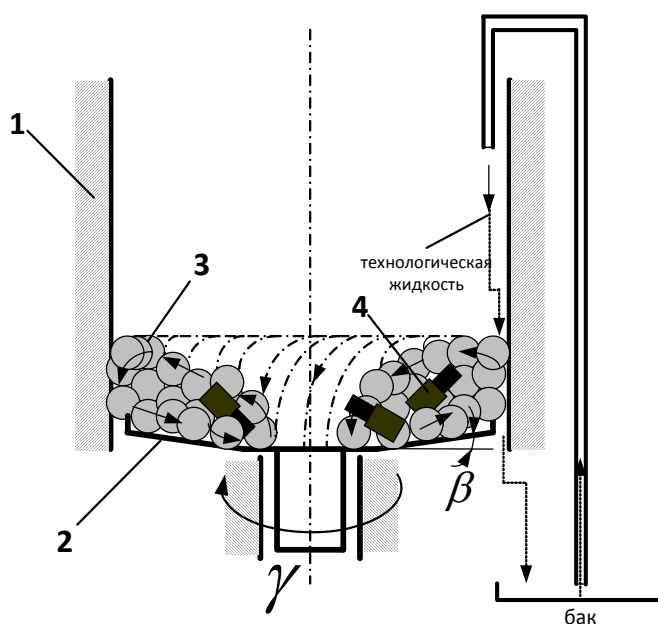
Схема процесса ОУ ЦРО (1 – рабочая камера, 2 – дно рабочей камеры; 3 – рабочая среда; 4 – обрабатываемые детали).
